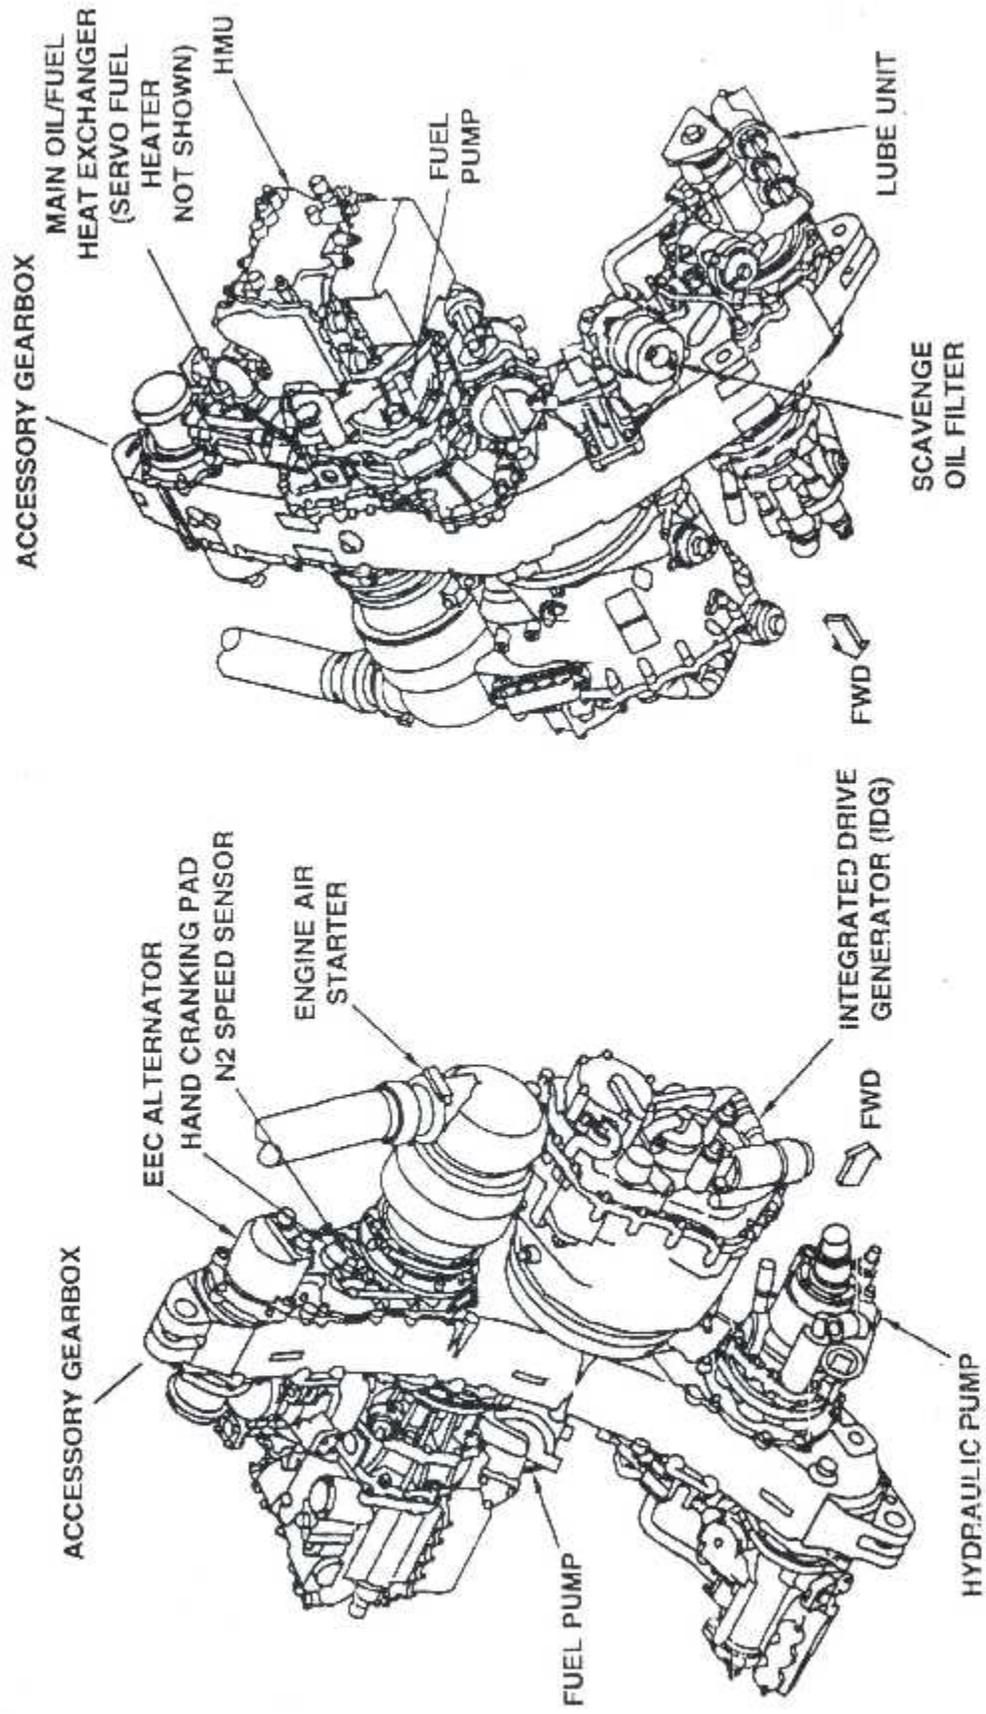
LES ACCESSOIRES DE LA GEARBOX (MODULE AGB)
